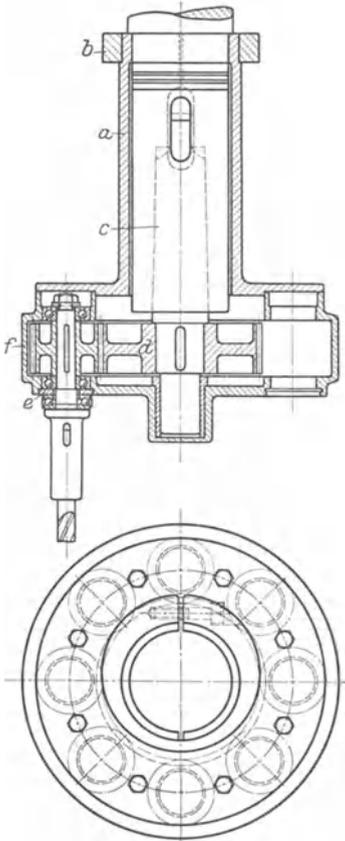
Mehrspindelbohrkopf auf Kugellager laufend. *a* Deckel mit Befestigungsschraube, wird an nicht umlaufender Bohrspindelhülse durch Klemmring *b* befestigt. *c* Kegelschaft mit treibendem Rad *d*, in Bohrspindel befestigt. *e* Gewindering in Gehäuse *f* befestigt.
